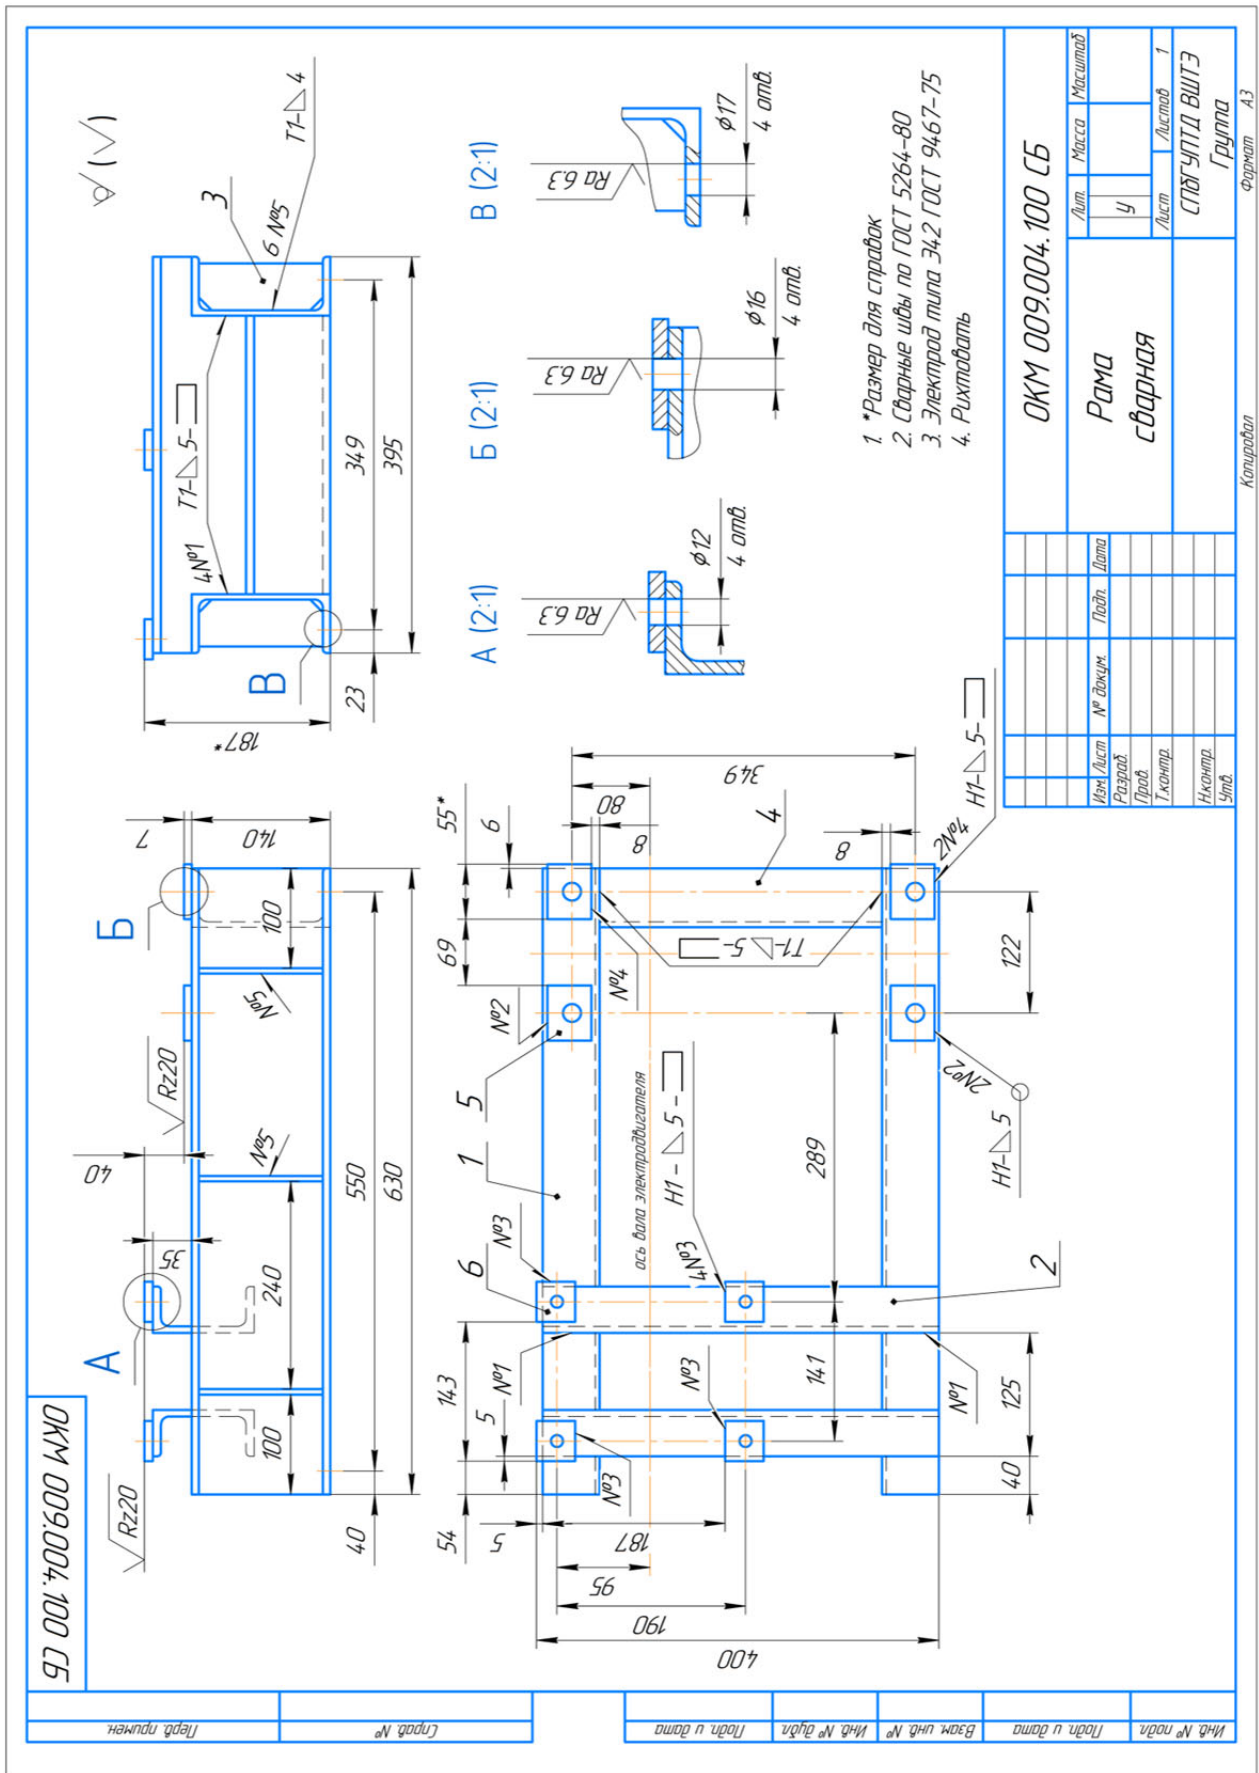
Пример чертежа сварной прямой рамы
